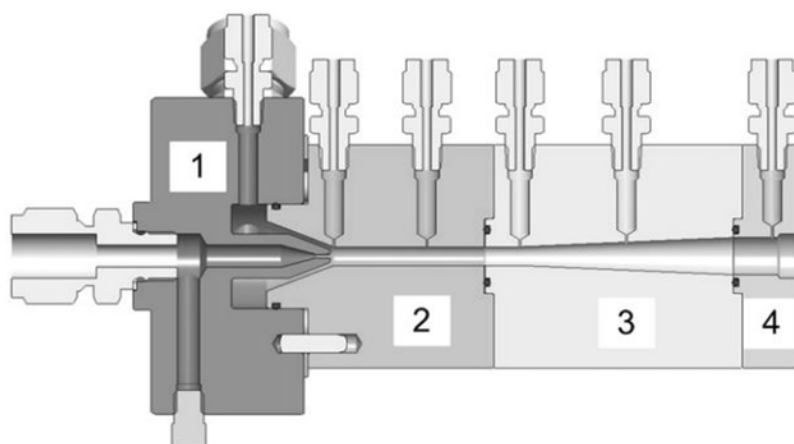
Struttura tipica di un eietttore. 1 - Sezione degli ugelli, 2 - Sezione di miscelamento, 3 - Sezione del diffusore, 4 - Sezione finale [18]
